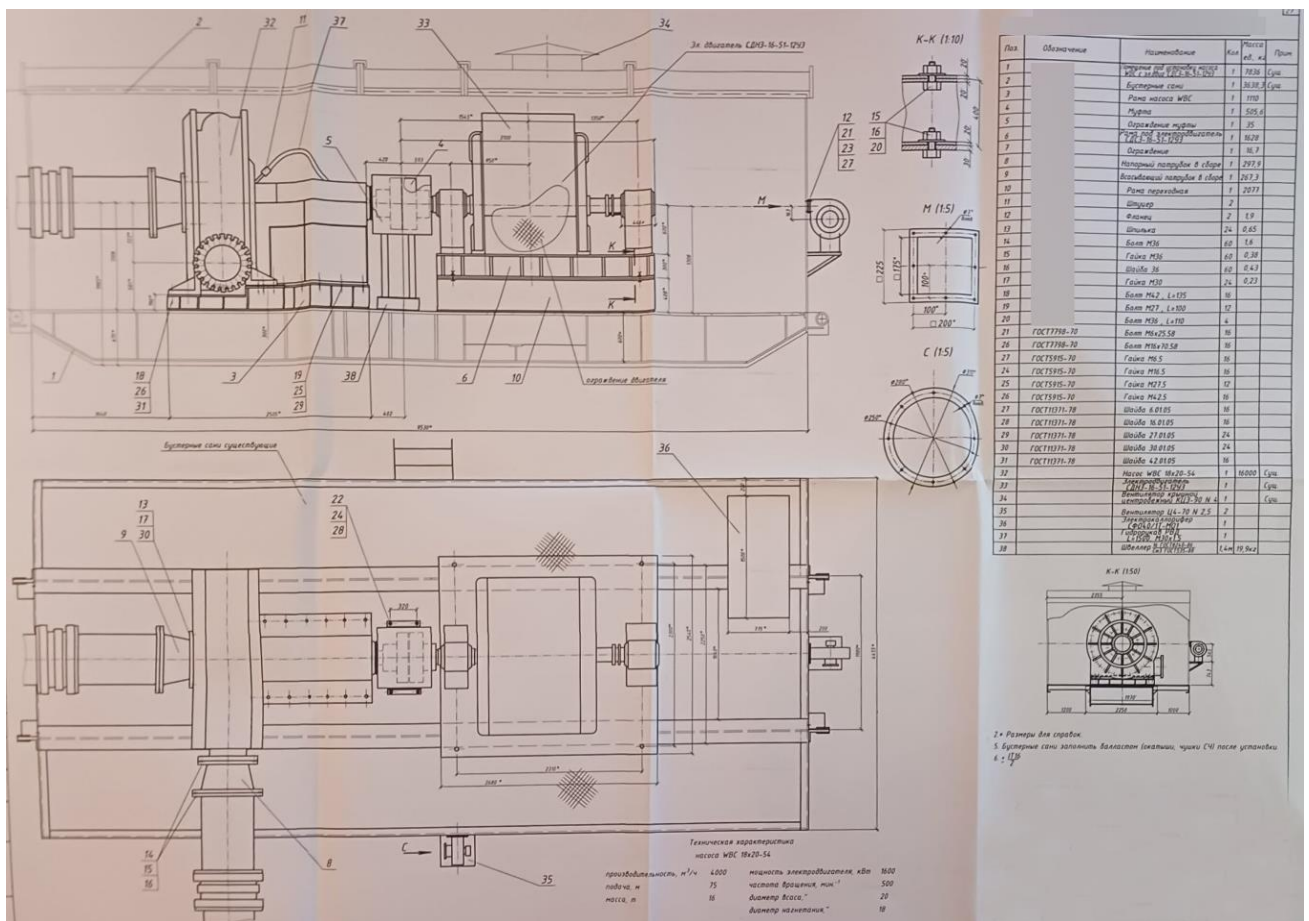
План, поздовжній і поперечний розрізи розміщення насоса Warman WBC 18x20 і електродвигуна СДН3-16-51-12у3 на фундаментній плиті
